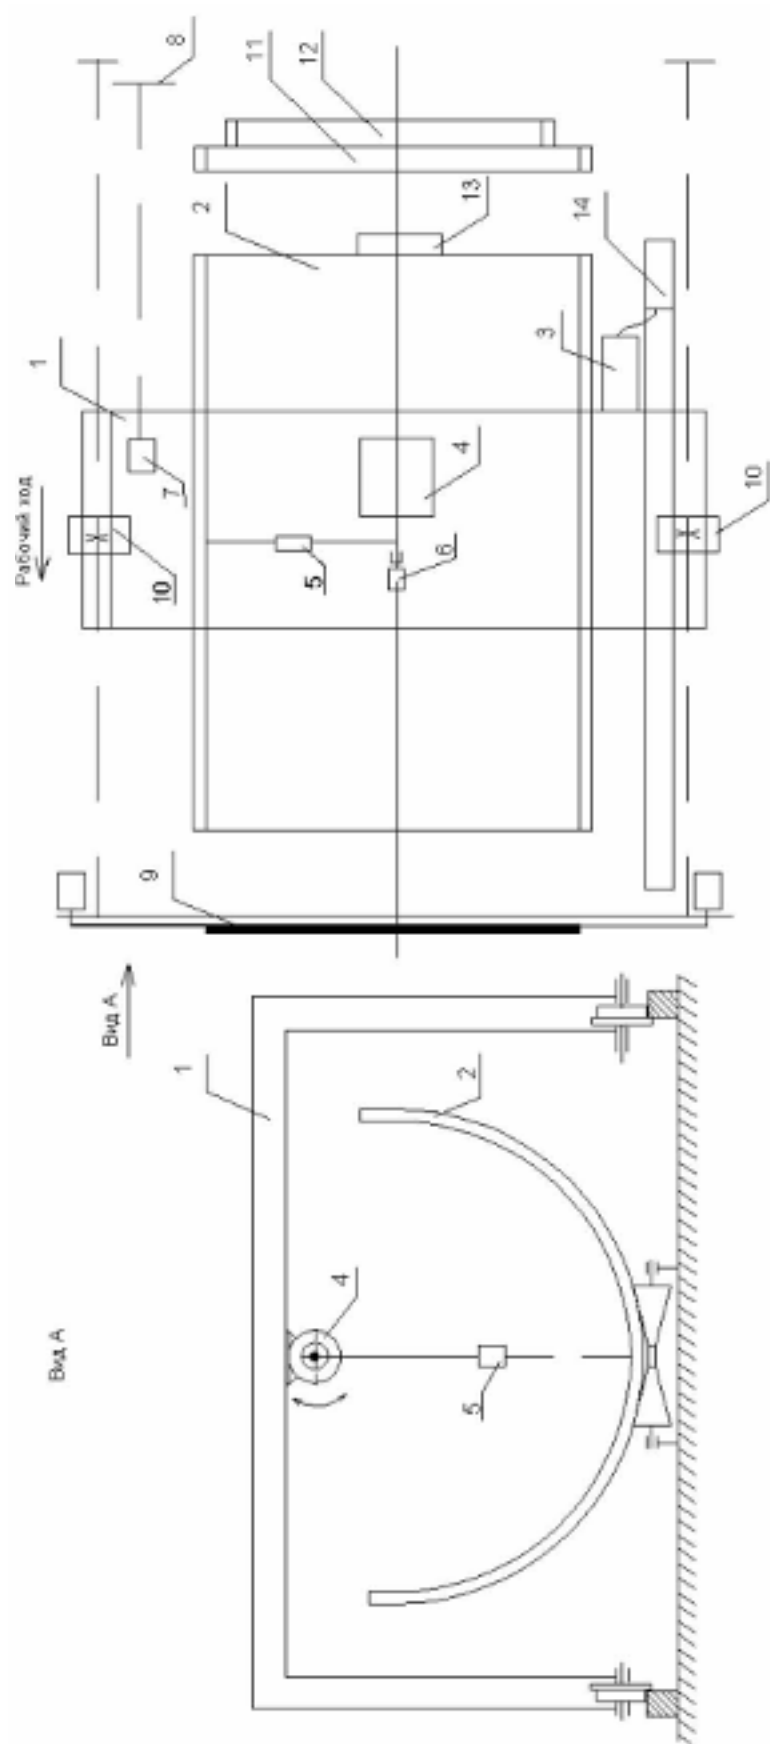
Кинематическая схема установки для контроля геометрии полуцилиндра. 1 – тележка; 2 – полуцилиндр; 3 – двигатель тележки; 4 – двигатель датчика; 5 – датчик; 6 – датчик измерения угла; 7 – устройство очистки от окалины; 8 – механизм стопорения; 9 – образец калибровки “1220°”; 10 – образец калибровки “1020°”; 11 – упор
